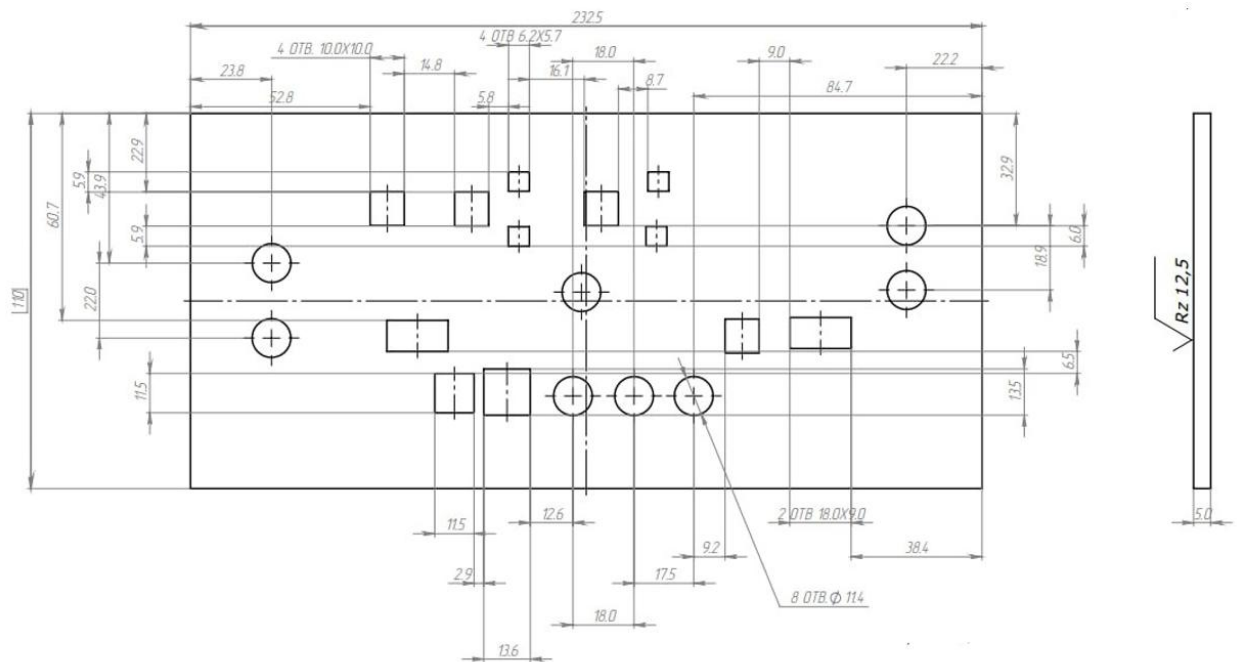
Креслення з розмірами верхньої частини корпусу
